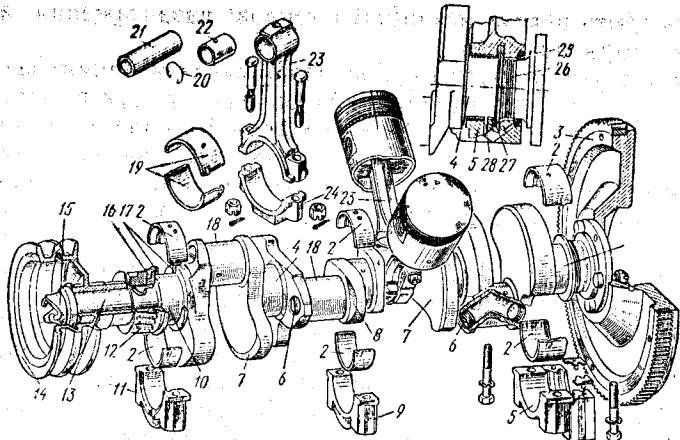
Деталі кривошипно-шатунного механізму двигуна ЗИЛ-130: 1 — поршень; 2 — вкладиші корінних підшипників колінчастого вала; 3 — маховик; 4 — корінна шийка колінчастого вала; 5 — кришка заднього корінного підшипника; 6 — пробка; 7 — противага; 8 — щока; 9 — кришка середнього корінного підшипника; 10 — передня шийка колінчастого вала; 11 — кришка переднього корінного підшипника; 12 — шестирня; 13 — носок колінчастого вала; 14 — шків; 15 — храповик; 16 — упорна шайба; 17 — біметалеві шайби; 18 — шатунні шийки колінчастого вала; 19 — вкладиші шатунного підшипника; 20 — стопорне кільце; 21 — поршневий палець; 22 — втулка верхньої головки шатуна; 23 — шатун; 24 — кришка шатуна; 25 — сальник; 26 — масловідгінна канавка; 27 — маслоскидний гребінь; 28 — дренажна канавка
